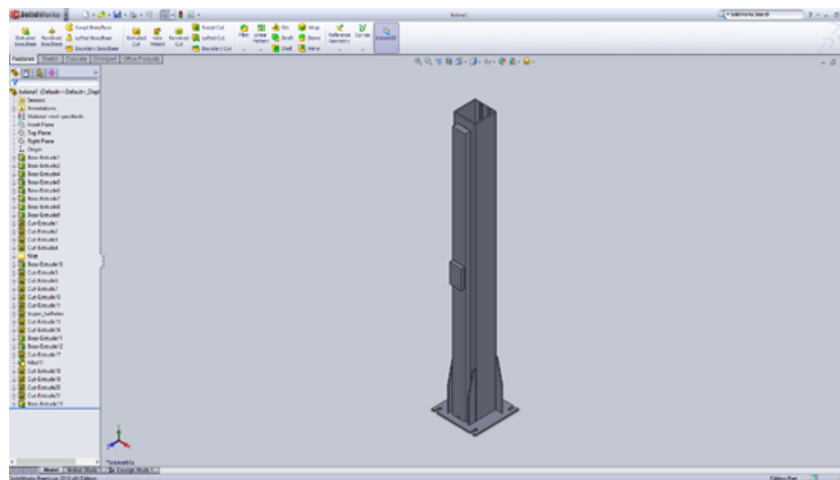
Δημιουργία αρχείου Assembly.
